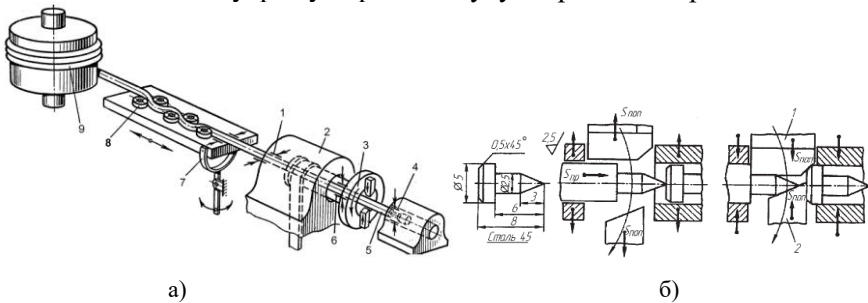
Схема роботи (а) і обробки заготовки (б) фасонно-відрізного автомата, що виготовляє деталі з дроту
